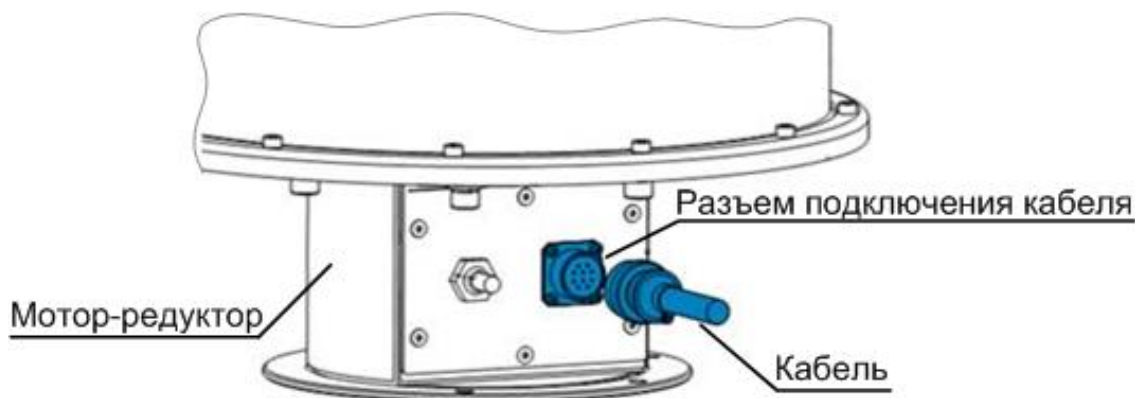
Крепление к мотор-редуктору кабеля сопряжения
